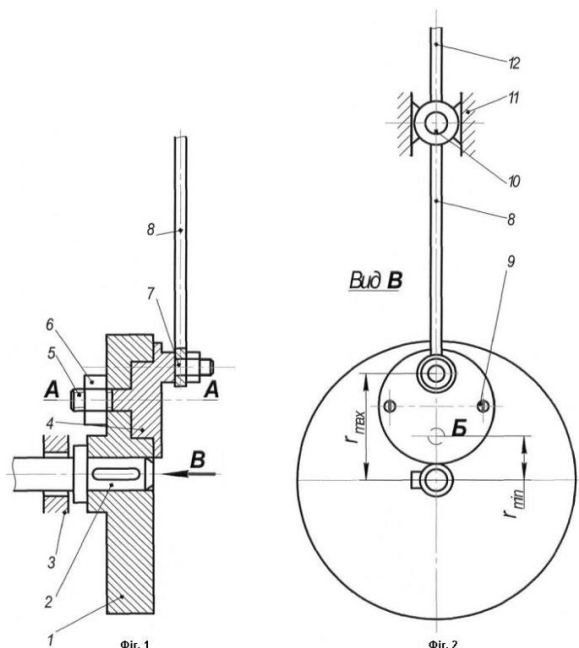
Ескіз до патенту 64057 «Регульований поршневий насос»: 1 - ведучий диск; 2 - ведучий вал; 3 - підшипник; 4 - кривошип циліндричної форми; 5 – вісь; 6 – гайка; 7 - палець кривошипа; 8 - шатун; 9 - гвинт; 10 - крейцкопф; 11 - напрямні крейцкопфа; 12 - шток; 13 - поршень; 14 - циліндр; 15,16 – впускні та випускні клапани.
